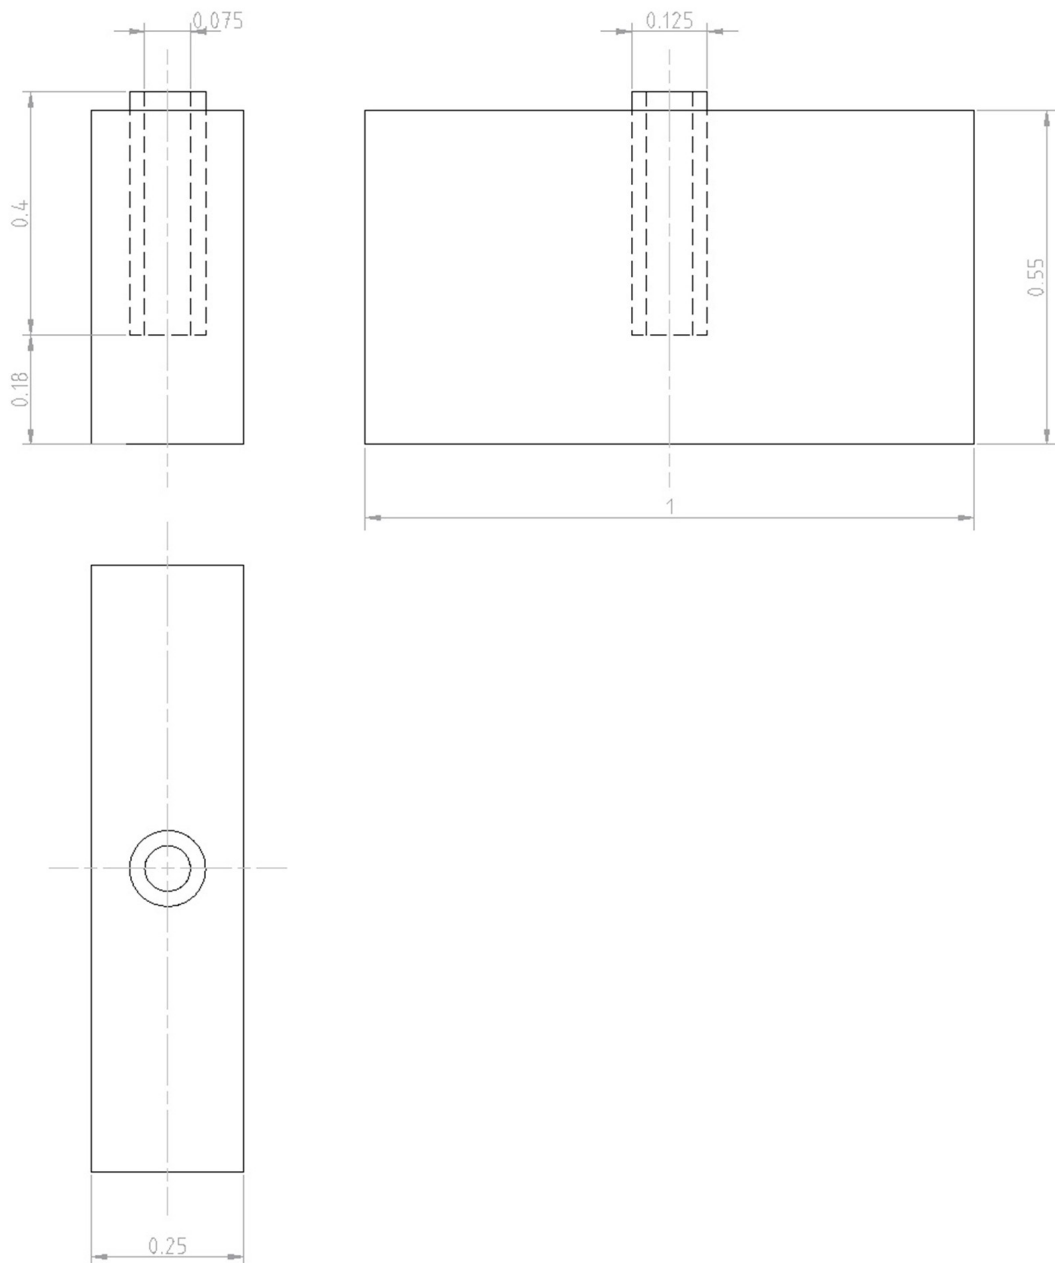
Alzado, perfil y planta acotados de la geometría. Se distingue el molde de forma paralelepípedica y, justo en el centro geométrico de su planta, la buza de forma tubular.
